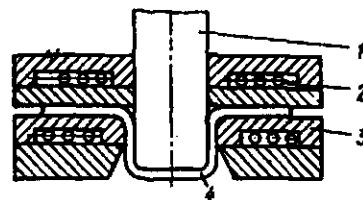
Схема вытяжки с нагревом: 1 – пуансон с водоохлаждающими каналами; 2 – электронагревательные элементы; 3 – матрица; 4 – заготовка
